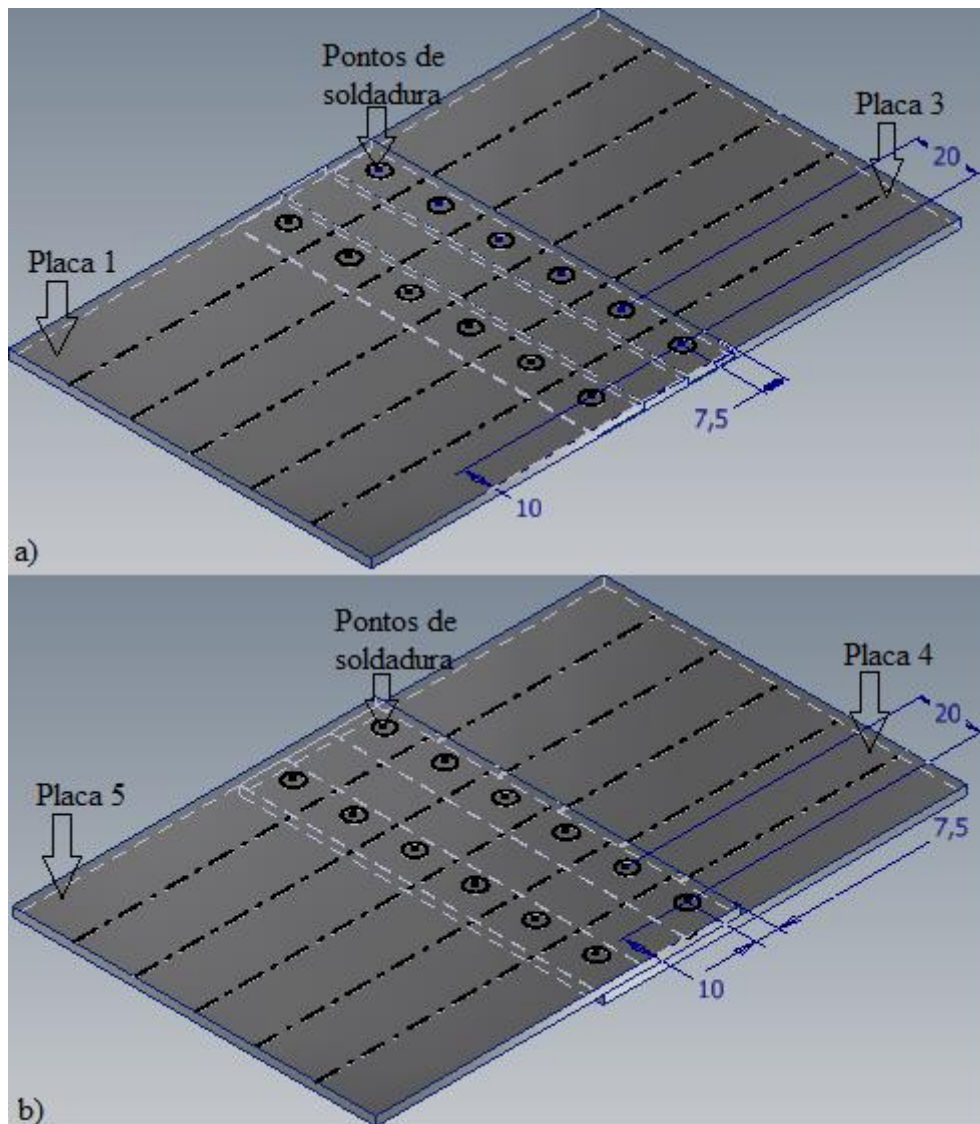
Pontos de aplicação da soldadura para obtenção dos provetes soldados: a) série 1 e b) série 2.
